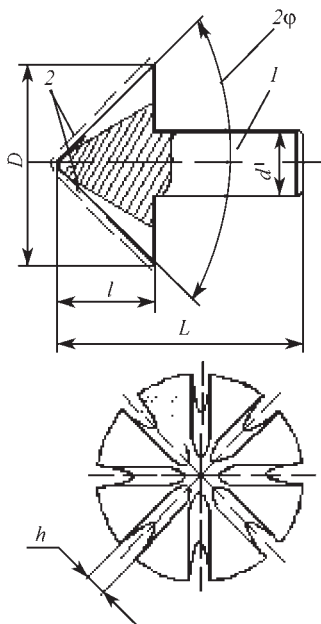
Конструкция алмазно-абразивной конической зенковки:
